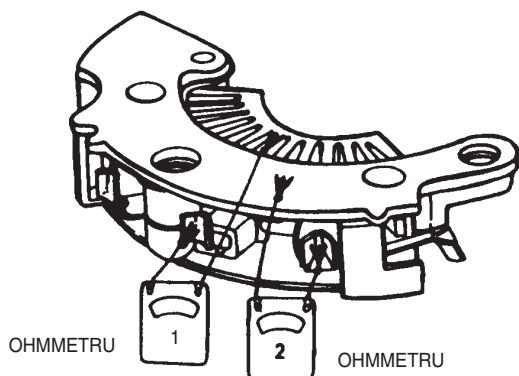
Alternatorul CS 130 - demontare, testare, montare
